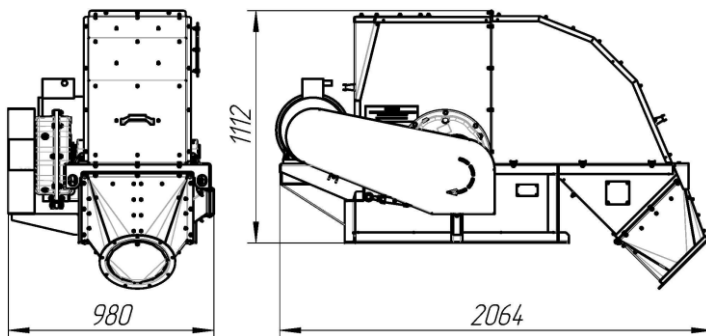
Станция приводная нории Н-100. Размеры габаритные
